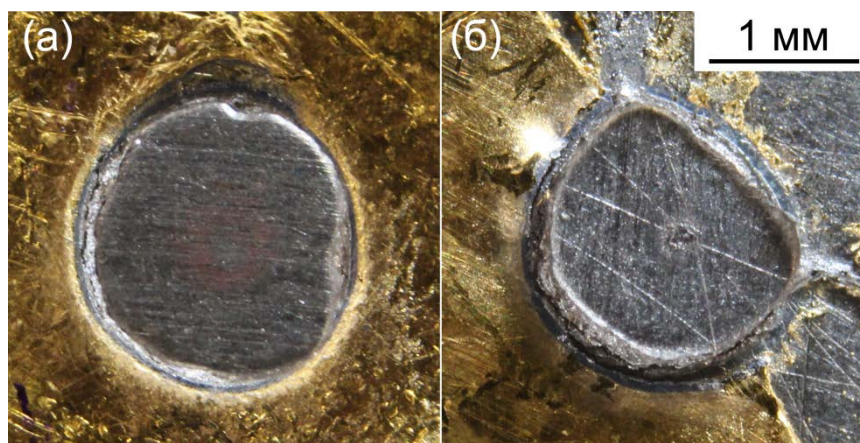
Общий вид сварных точек после отрыва титановой пластины:
